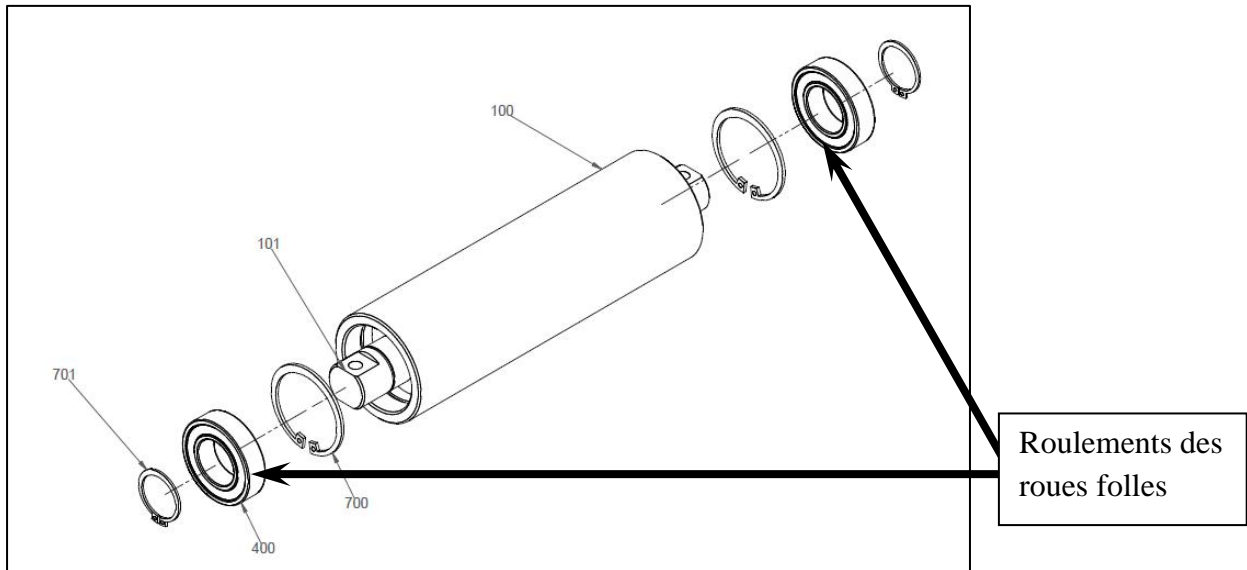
Vue éclatée d'une des roues libres du Final Forming
